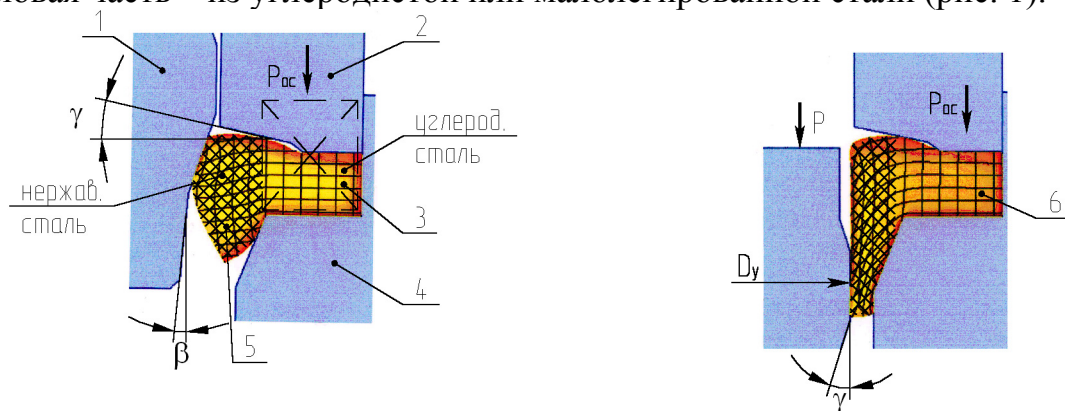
Схема действия инструмента для операции осадки и отбортовки при штамповке биметаллического воротникового фланца:
